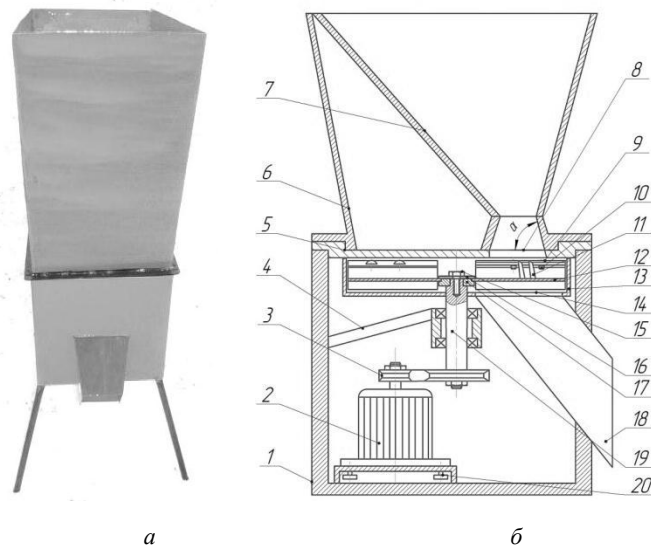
Измельчитель корнеклубнеплодов: а – общий вид; б – конструктивно-технологическая схема; 1 – корпус; 2 – электродвигатель; 3 – ременная передача; 4 – кронштейн крепления опорных подшипников; 5 – крышка; 6 – загрузочный бункер; 7 – наклонная перегородка; 8 – загрузочное окно; 9 – горизонтальный нож; 10 – винт; 11 – вертикальный нож; 12 – режущий диск; 13 – отбойник; 14 – выгрузное окно; 15 – винт; 16 – прижимная шайба; 17 – посадочная шайба; 18 – выгрузная горловина; 19 – приводной вал; 20 – натяжное устройство
